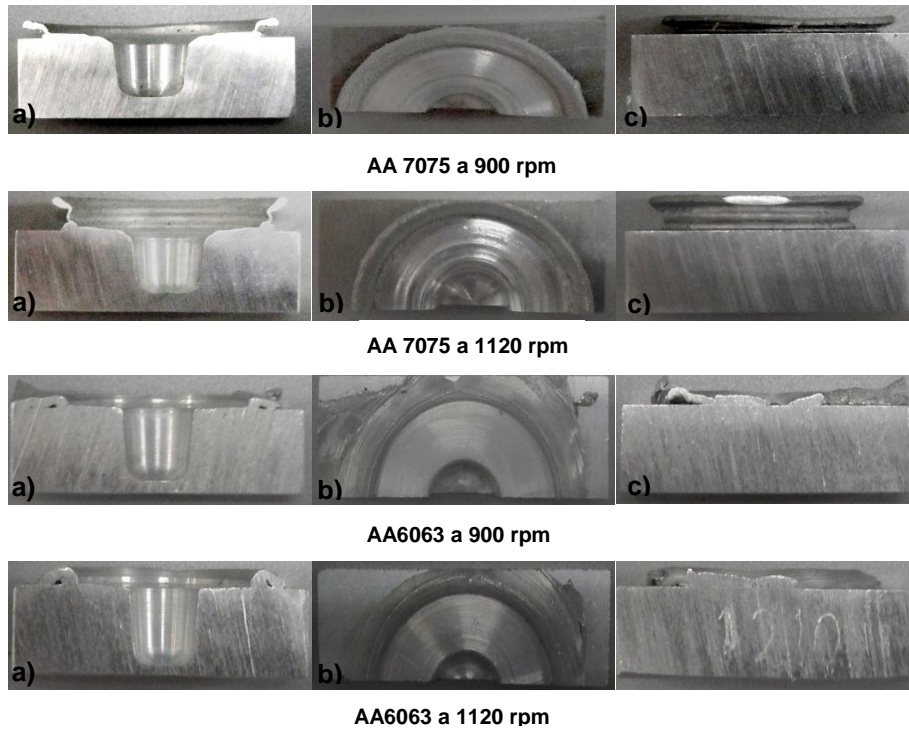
Puntos de soldadura de AA7075a 900 y 1120 rpm y AA6063 a 900 y 1120 rpm, a) vista transversal, b) vista superior y c) vista lateral. Fuente propia.
